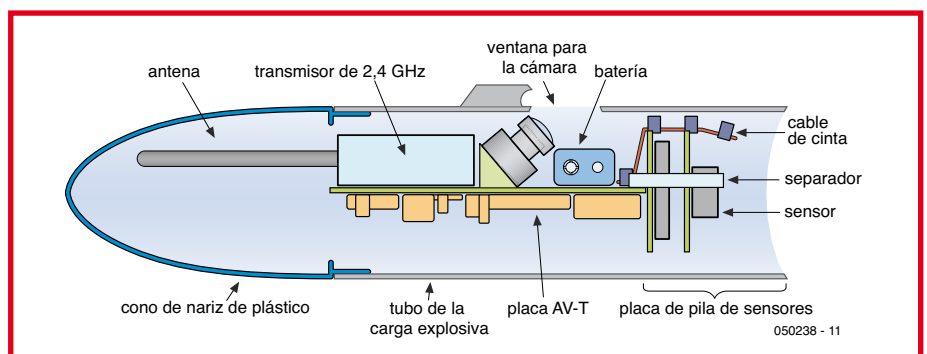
Corte lineal de la carga explosiva que nos muestra un ejemplo de montaje dentro del cohete.
